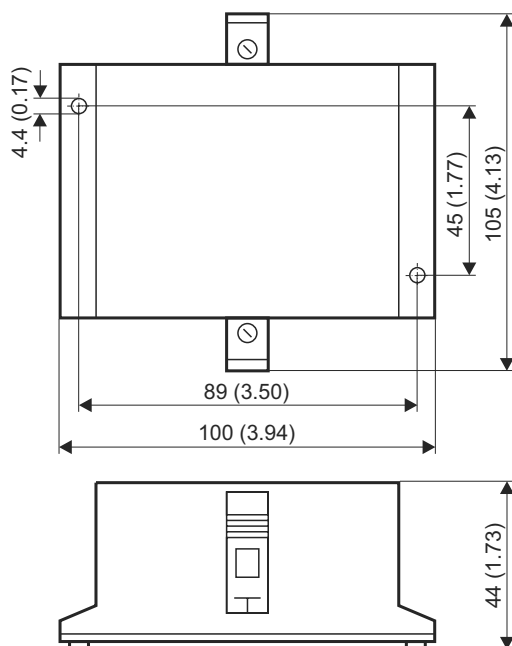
Dimensões DCD12A, dimensões em mm (in)
